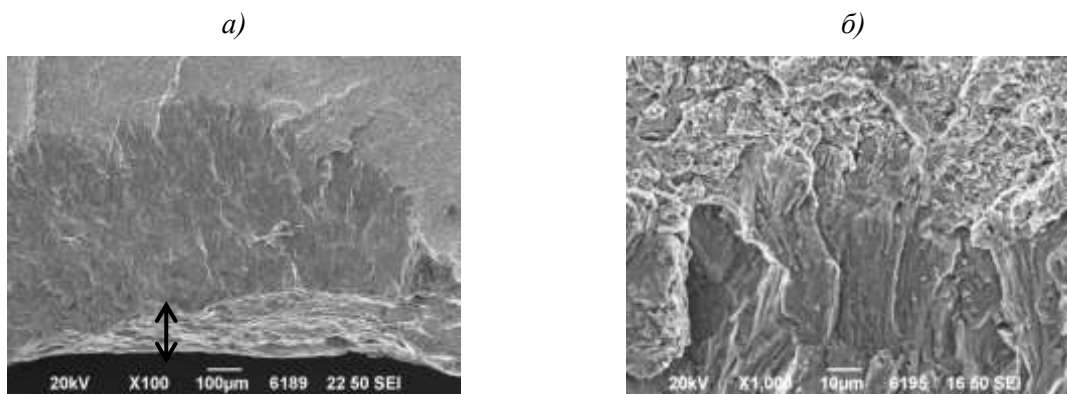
Строение вскрытой трещины на дорожке качения наружного кольца подшипника № 1. а – развитие усталостной трещины от выкрашиваний на дорожке качения.
